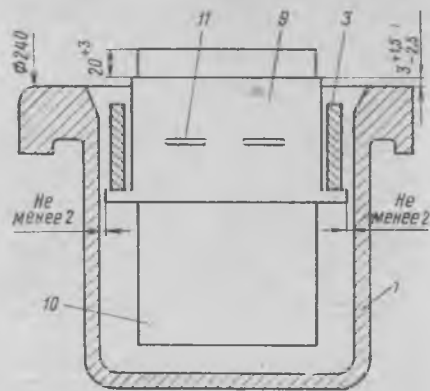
Устройство для смазки моторно-осевого подшипника электродвигателя ЭД107А:
